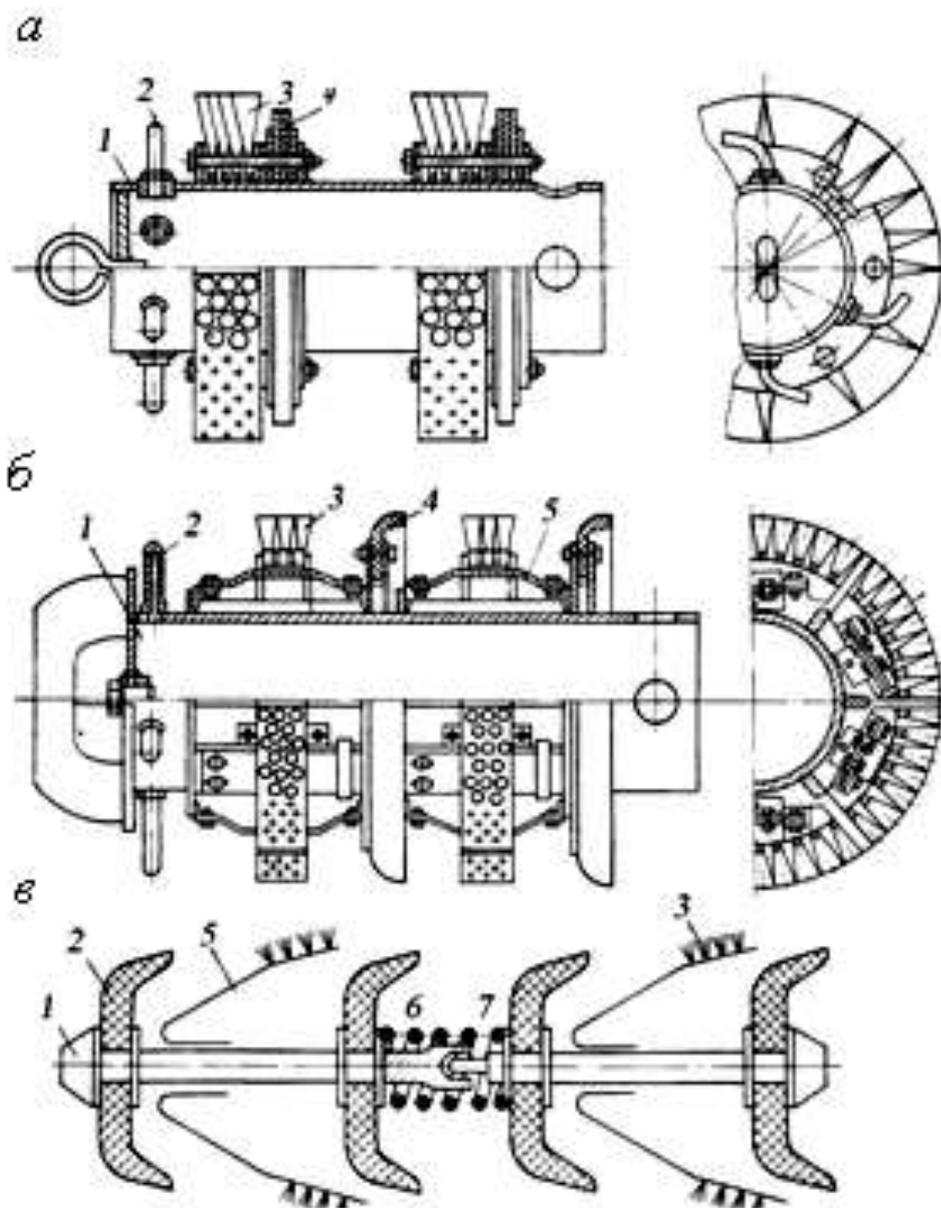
Конструктивные схемы очистных поршней: а – с прямыми манжетами и жестким креплением металлических щеток; б – с самоуплотняющимися манжетами и упругим креплением металлических щеток; в – сочлененного типа; 1 – корпус; 2 – реактивная труба; 3 – металлические щетки; 4 – манжета; 5 – упругая пластина; 6 – пружина цилиндрическая; 7 – шарнирное сочленение
